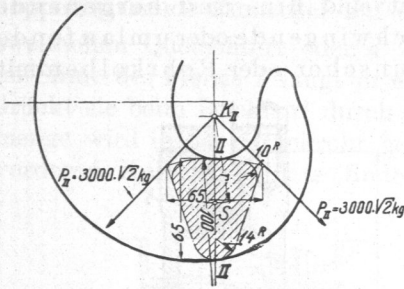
Berechnung des Querschnittes II—II des Hakens Abb. 53b nach Tolle. M. 1: 5.
